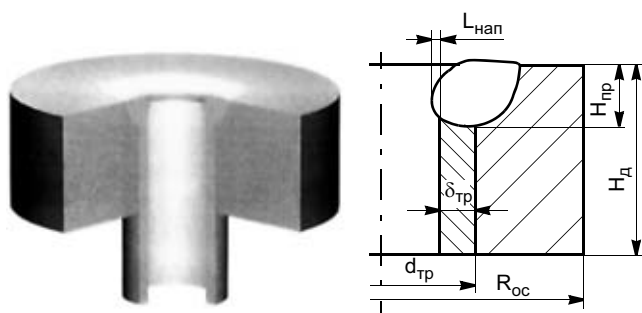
Заводской опытный образец для подбора оптимальных режимов сварки
